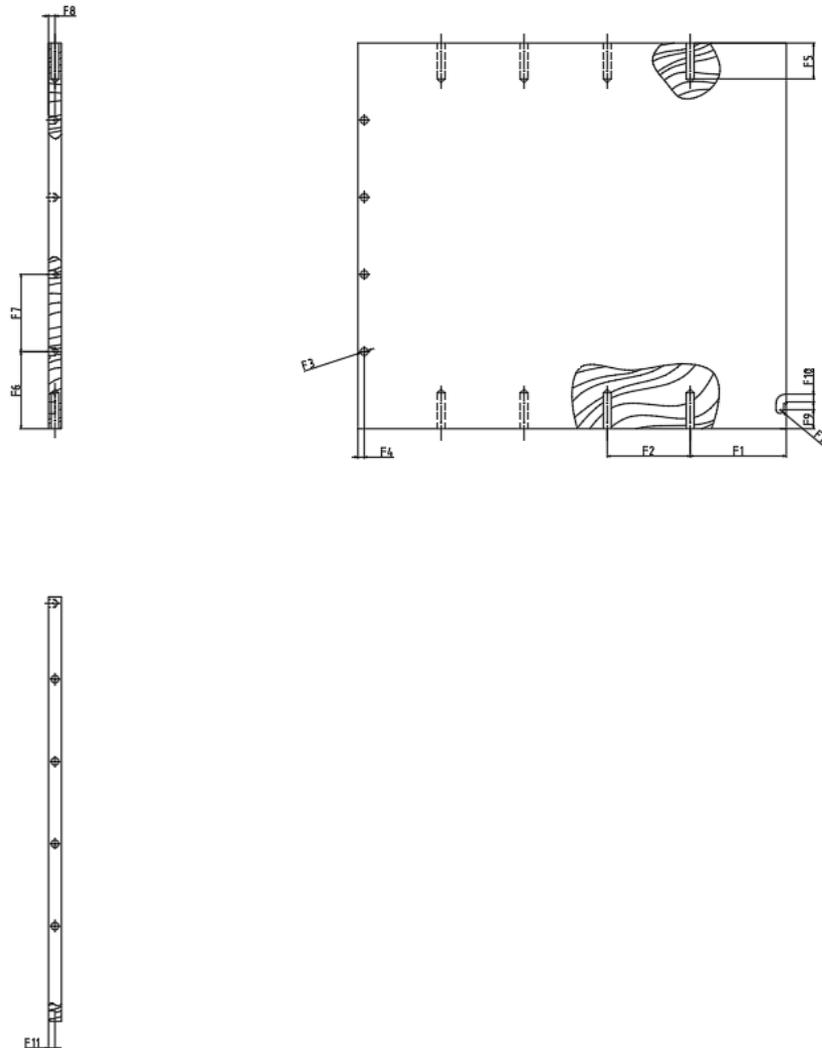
Plano Dimensionado Previo del Lateral Derecho Cajón 2.1.3
